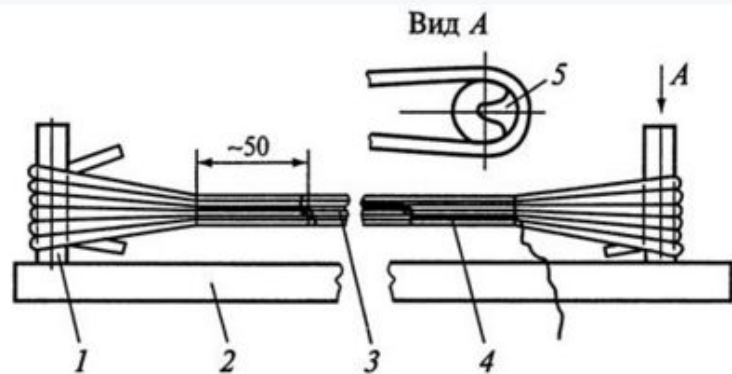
Приспособление для заготовки проводов одинаковой длины и вязки их в жгут:
